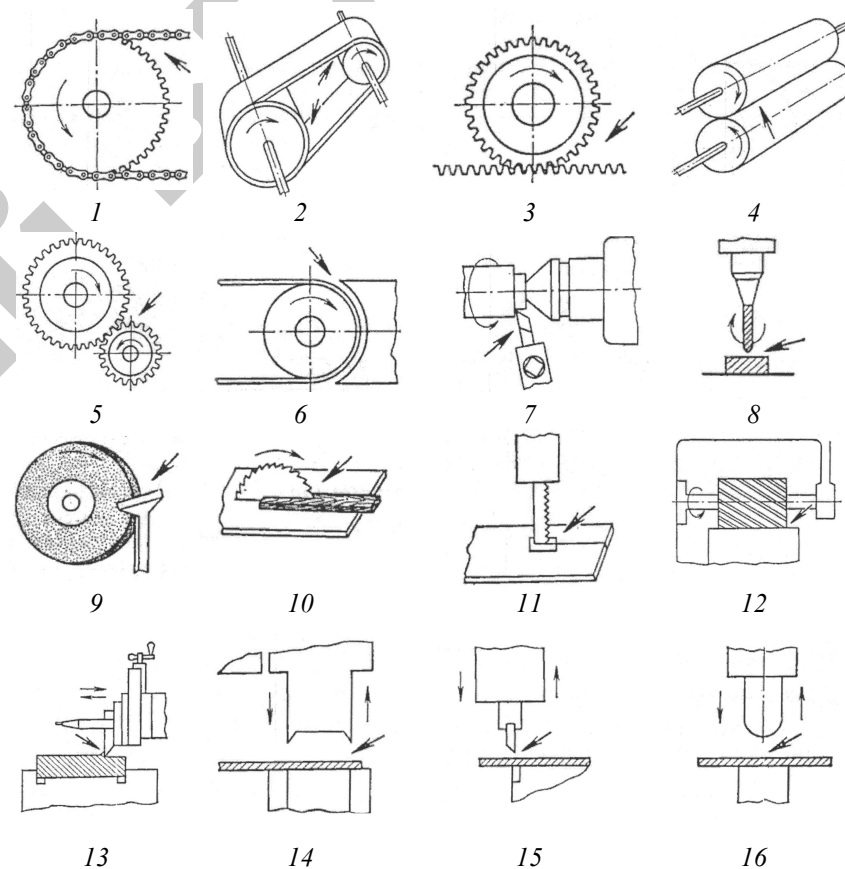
Опасные зоны механизмов (указаны жирной стрелкой): 1 – передаточная цепь с зубчаткой; 2 – ременная передача; 3 – зубчатая рейка; 4 – вальцы; 5 – зубчатые колеса; 6 – конечный узел ленточного конвейера; 7 – суппорт токарного станка; 8 – сверло; 9 – абразивный круг; 10 – циркулярная пила; 11 – ленточная пила; 12 – фреза; 13 – резец поперечно-строгального станка; 14 – штамп; 15 – отрезное устройство; 16 – выдавливающее устройство
